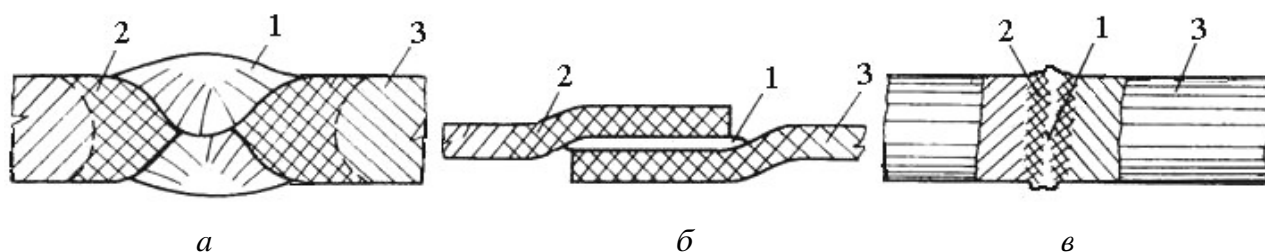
Схема строения соединений, выполненных: а – сваркой плавлением: 1 – литой металл шва, 2 – зона термического влияния (ЗТВ), 3 – основной металл; б – пайкой: 1 – металл шва, 2 – ЗТВ, 3 – основной металл; в – сваркой давлением: 1 – зона соединения, 2 – зона термомеханического воздействия, 3 – основной металл
